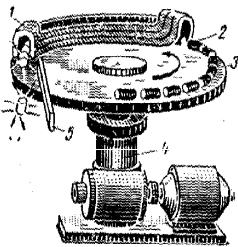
Схема карусельного нагревателя с щелевым индуктором:
